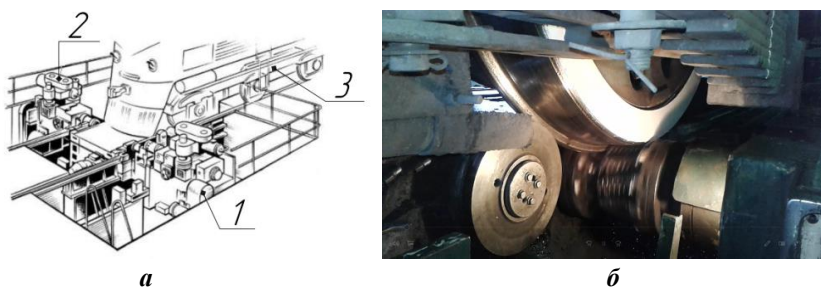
а) общий вид станка КЖ-20 для обточки бандажей колесных пар без выкатки, б) станок КЖ-20 в работе в ТЧЭ Лоста, 1 - электродвигатель станка; 2 - суппорт; 3 - рама тележки
